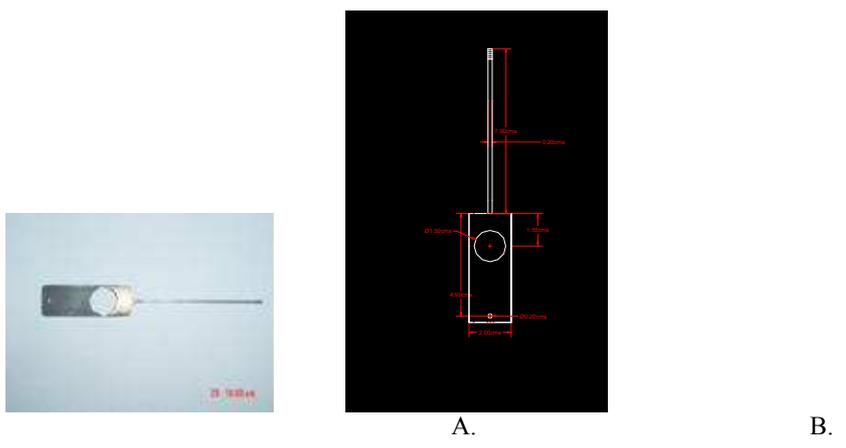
Placa semillera con extensión para sujetar al cable. (A. Diseño definitivo, B. Dimensiones).
